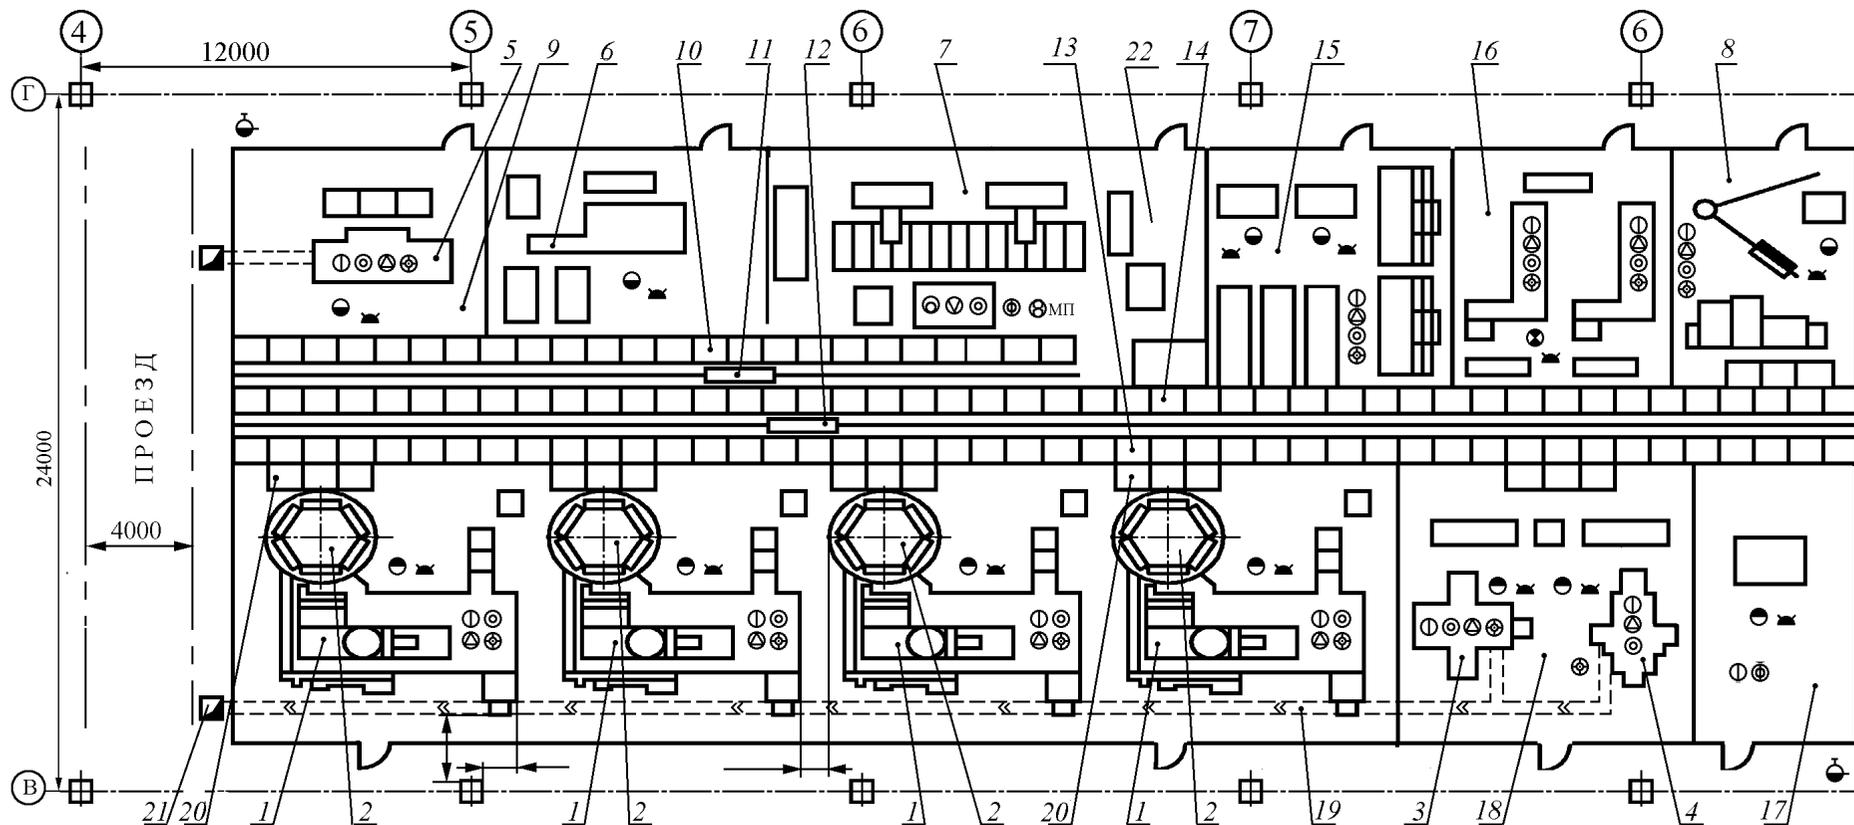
П14. ГПУ для обработки корпусных деталей с единой АТСС:
